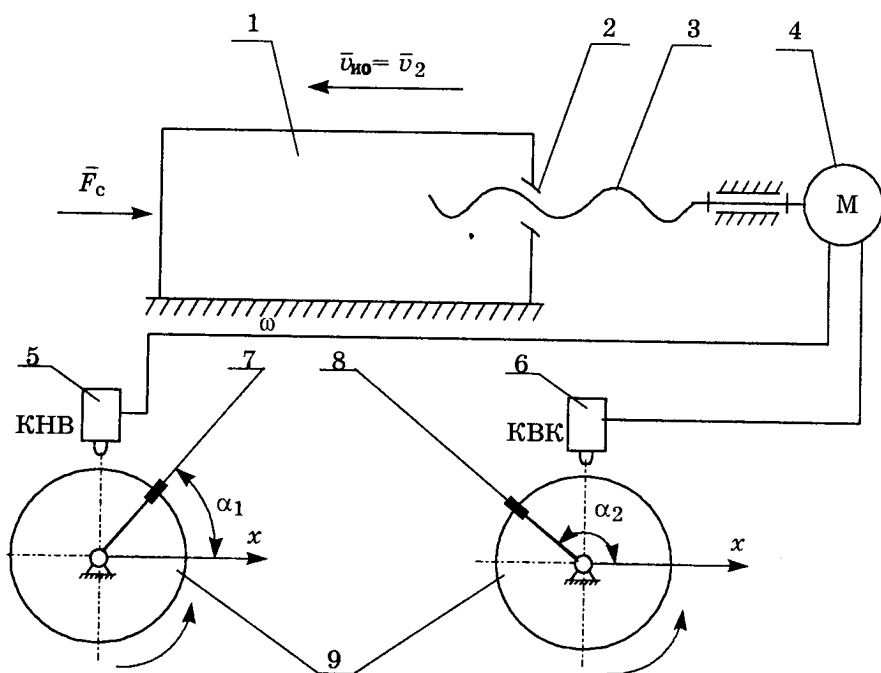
Управление перемещением с помощью командоаппарата: 1 — исполнительный орган; 2 — гайка; 3 — винт; 4 — двигатель; 5, 6 — конечные выключатели начала (КВН) и конца (КВК) хода рабочего органа; 7, 8 — кулачки (упоры) на командоаппарате; 9 — барабан с кулачками (командоаппарат)
